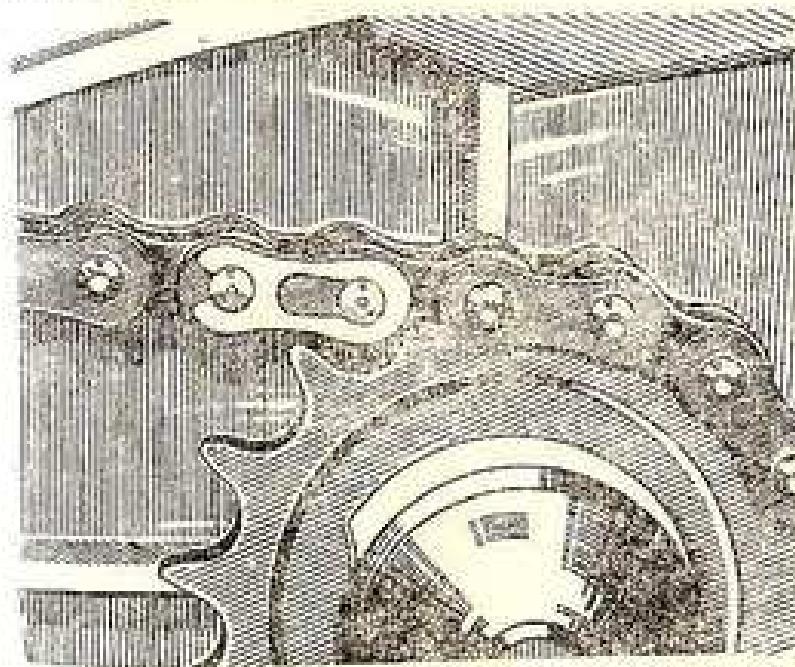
УСТАНОВКА ЗАЩЕЛКИ ЗАМКА ЦЕПИ
